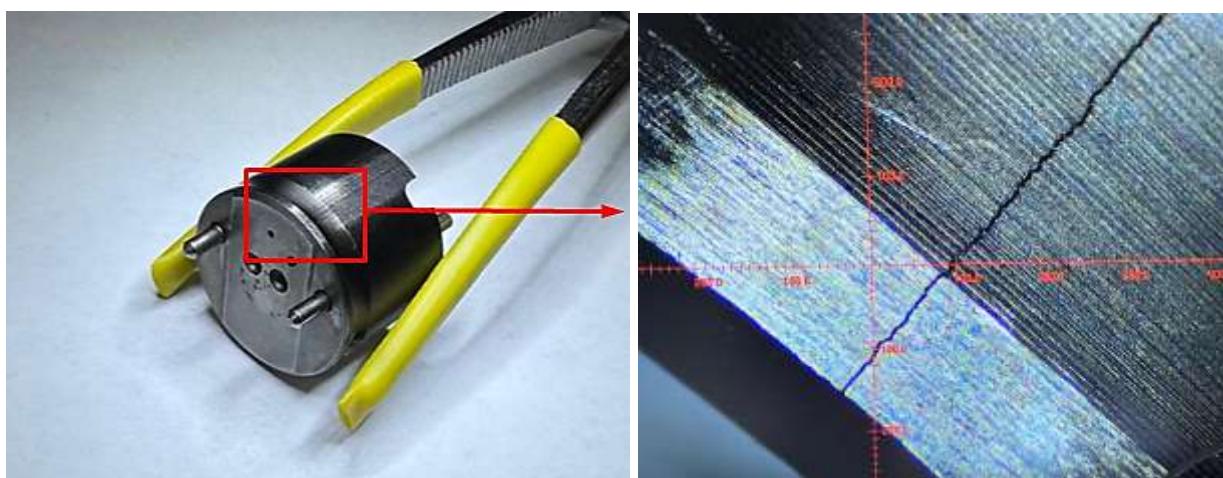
, 4 - Трещина обратного клапана (мультиплликатора) топливной форсунки 3-го цилиндра ДВС
